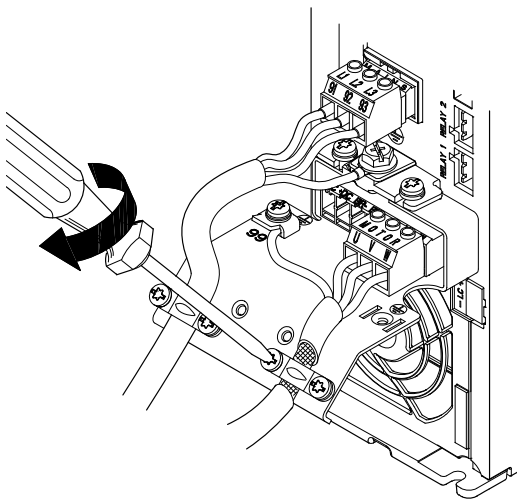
Anschließen des Motorsteckers und Auflegen des abgeschirmten Kabels
